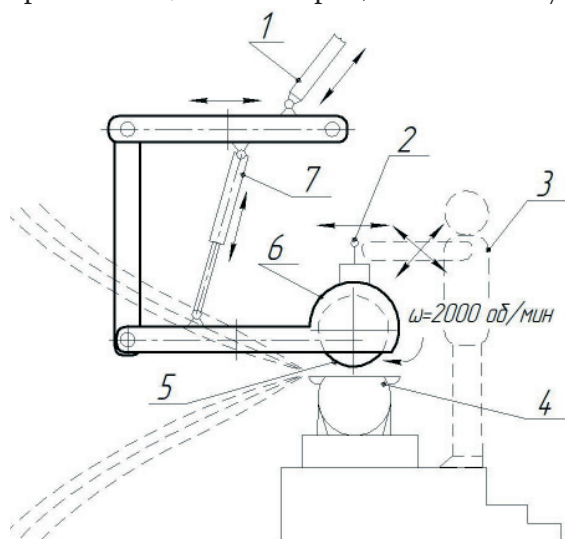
Схема машины для очистки отливок ОЛВ-26ВП: 1 – гидроцилиндр продольного перемещения головки; 2 – джойстик; 3 – оператор; 4 – отливка; 5 – круг абразивный; 6 – головка; 7 – гидроцилиндр вертикального перемещения головки
